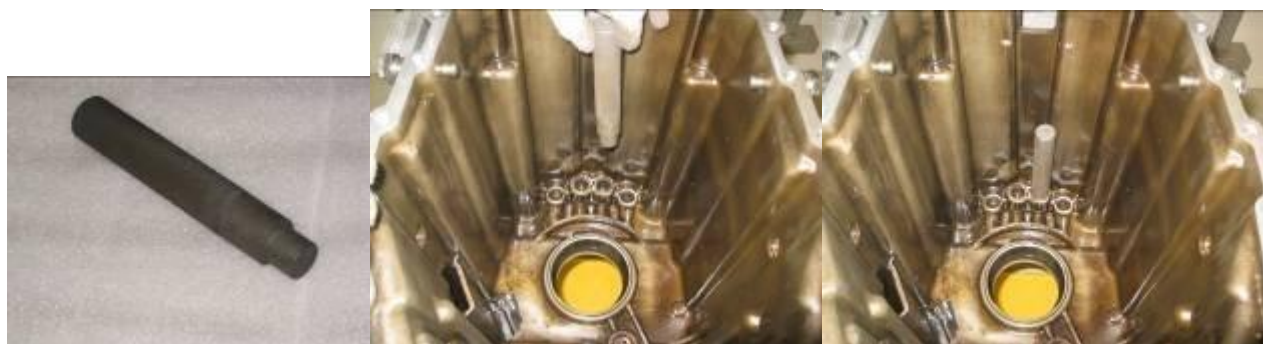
Оправка И801.101.000 Установка игольчатого подшипника в картер КП
